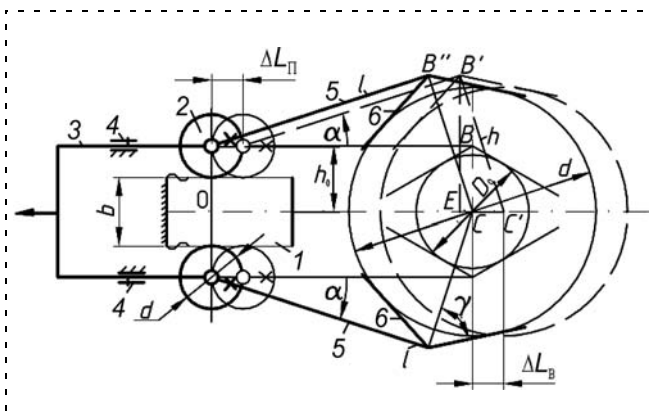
Преобразователь движения мехатронного модуля захватного устройства с подвижными колесами
